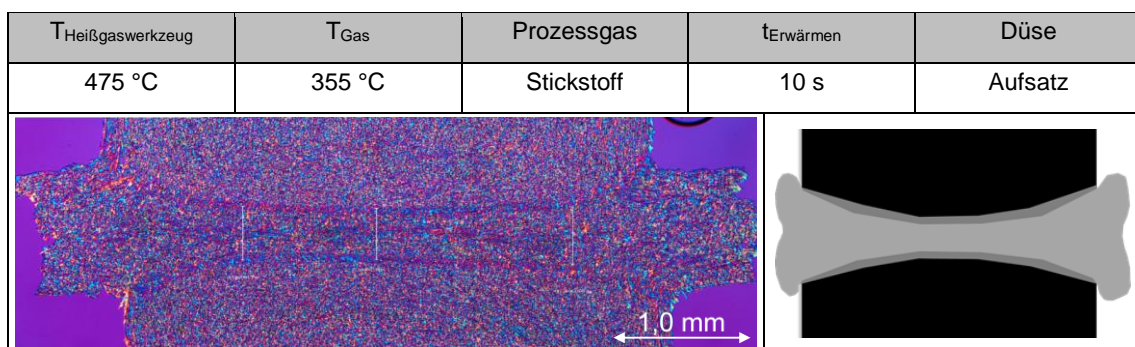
Dünnschnittaufnahme einer mit Aufsatz-Düse erwärmten Schweißnaht mit einem mit dem Heizelementschweißen vergleichbaren aufgeschmolzenen Fügebereich
